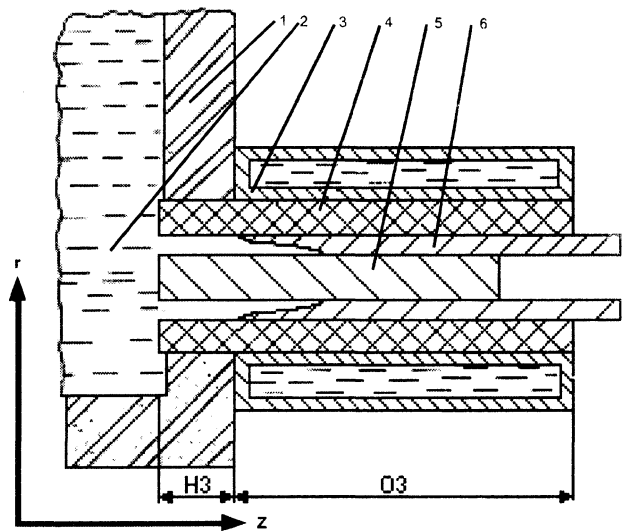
Схема непрерывного литья трубной заготовки: 1 — металлоприемник; 2 — расплав; 3 — металлический кристаллизатор; 4 — графитовая втулка; 5 — дорн; 6 — отливка
